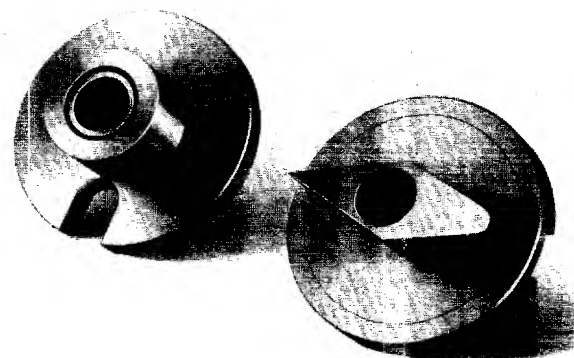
Galet sur tenon RP 102 et traceur RP 103
